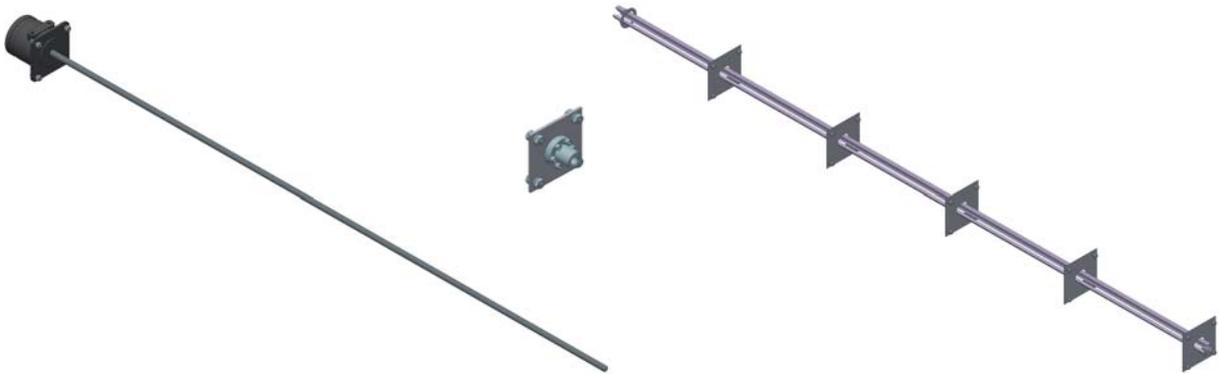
Komponenten eines Spindeltriebs: Spindel mit Motor, Spindelmutter, Spindelführung (v.l.n.r.)
